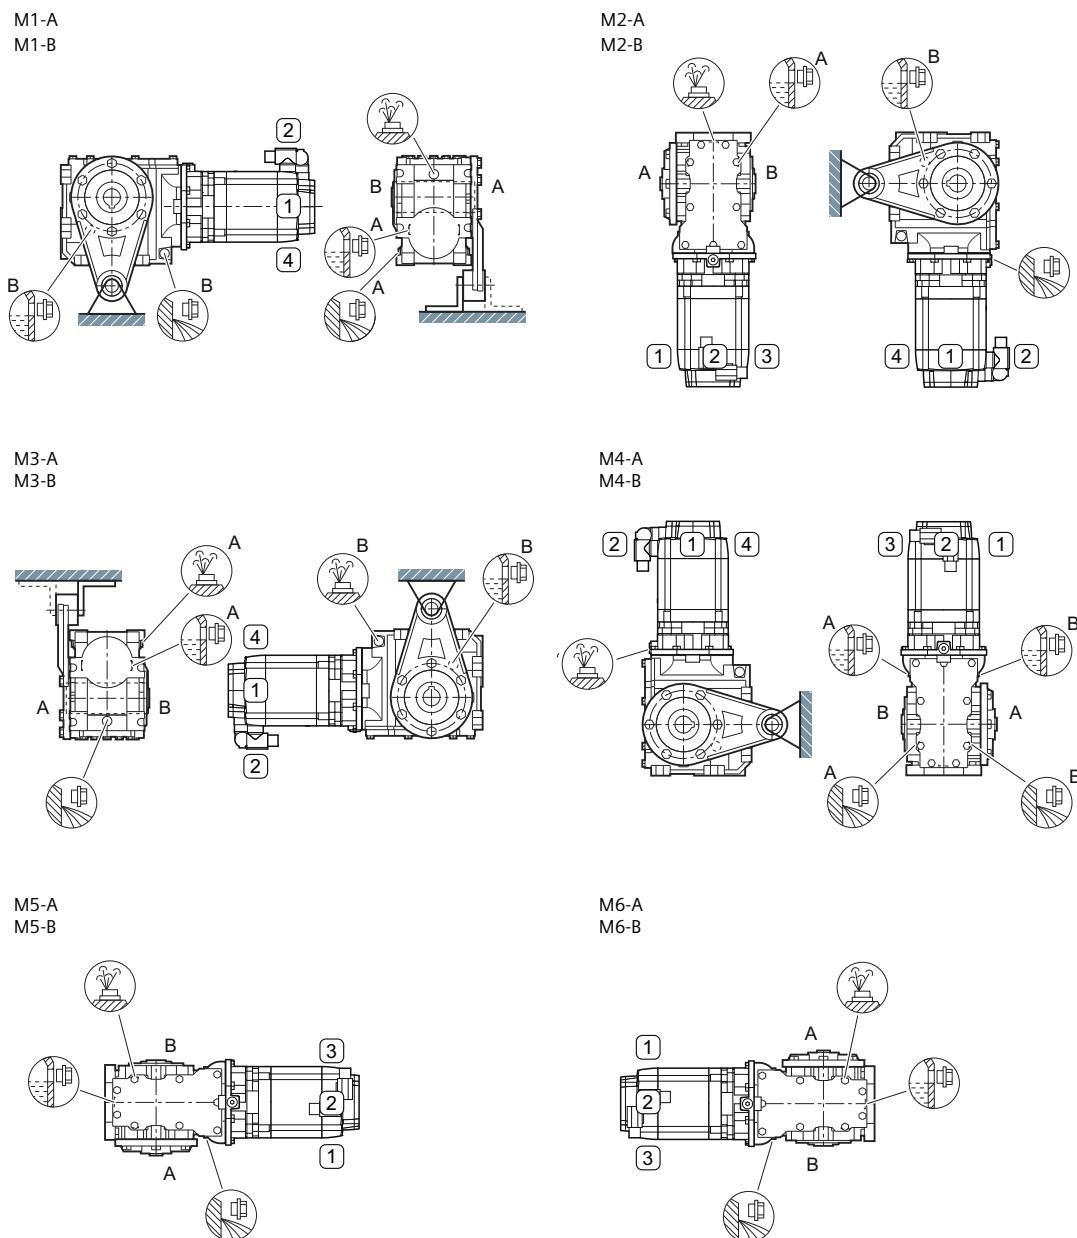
Einbaulagen für Servo-Stirnradschneckengetriebemotor CAD, Aufsteckausführung, Baugröße 39A, 2-stufig
